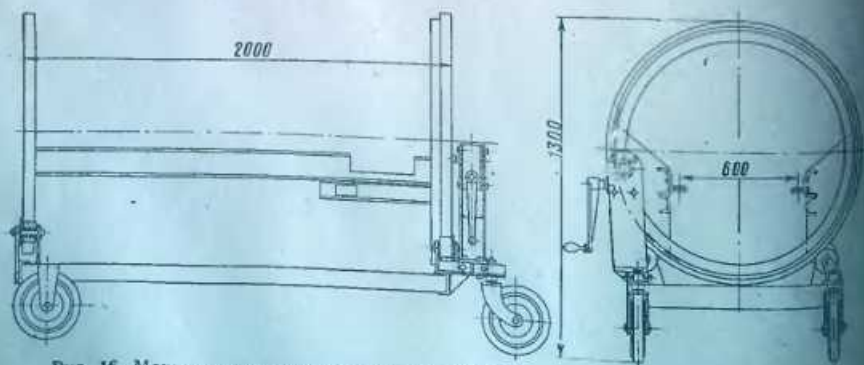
Монтажная поворотная тележка ЛМ9690-222 для разборки и сборки дизеля
